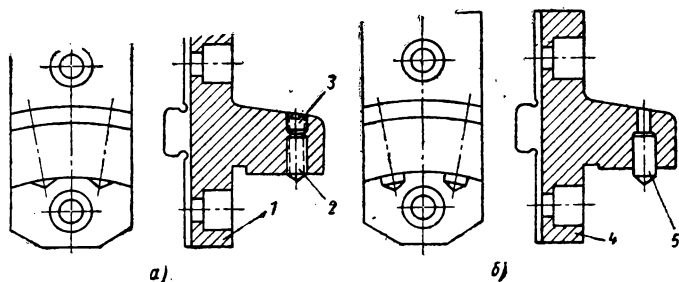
Установка в двухкулачковом патроне детали сложной формы.
